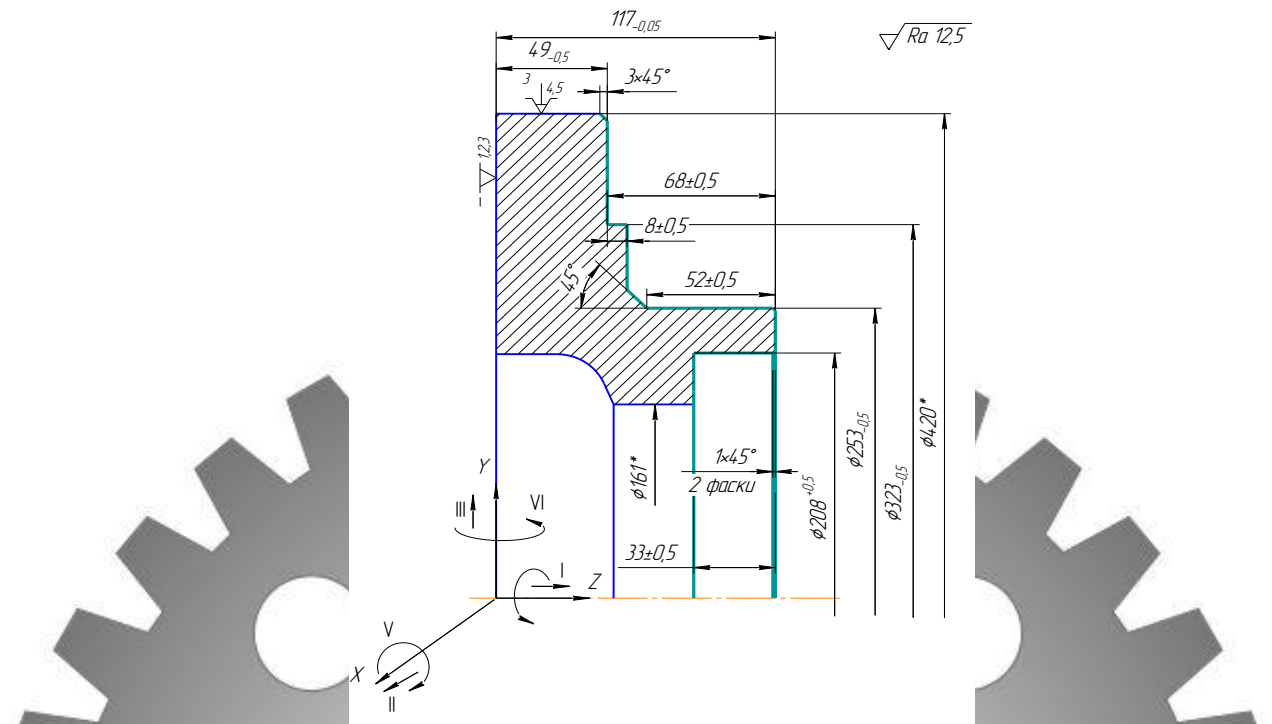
Схема базування деталі на токарній з ЧПК операції 020
